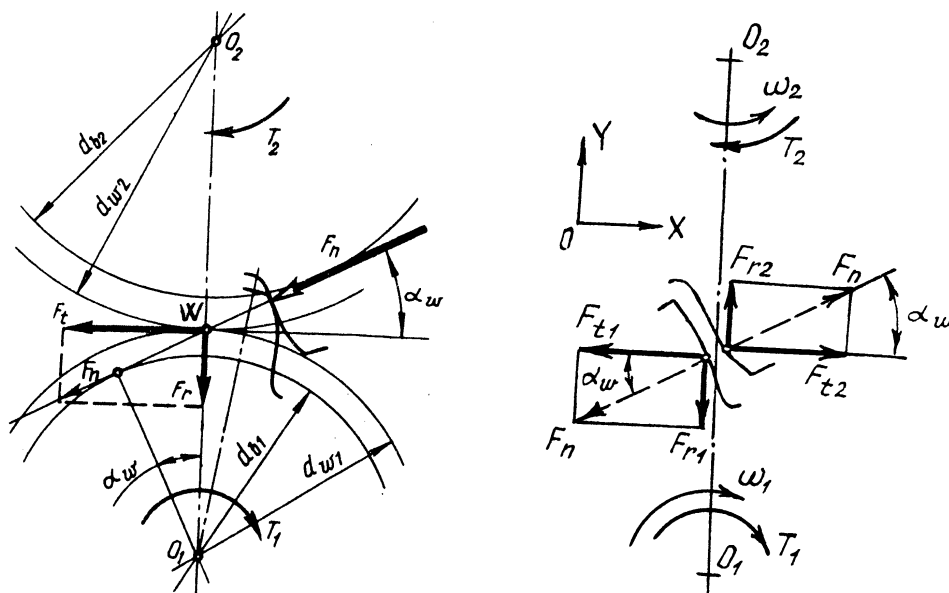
Силы в зацеплении цилиндрической прямозубой передачи
